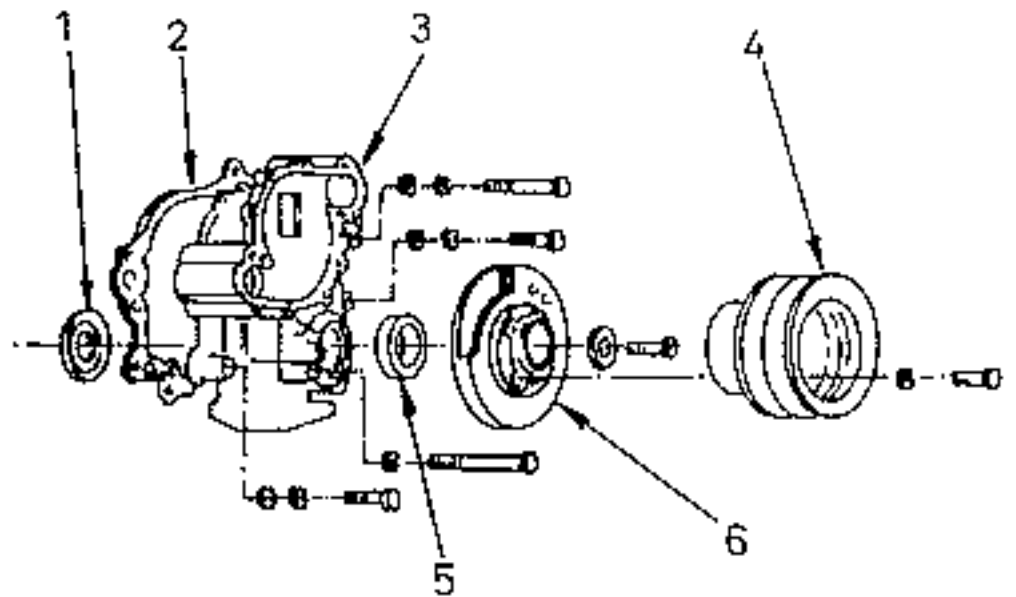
Die Teile des Steuerdeckels eines V8-Motors.
